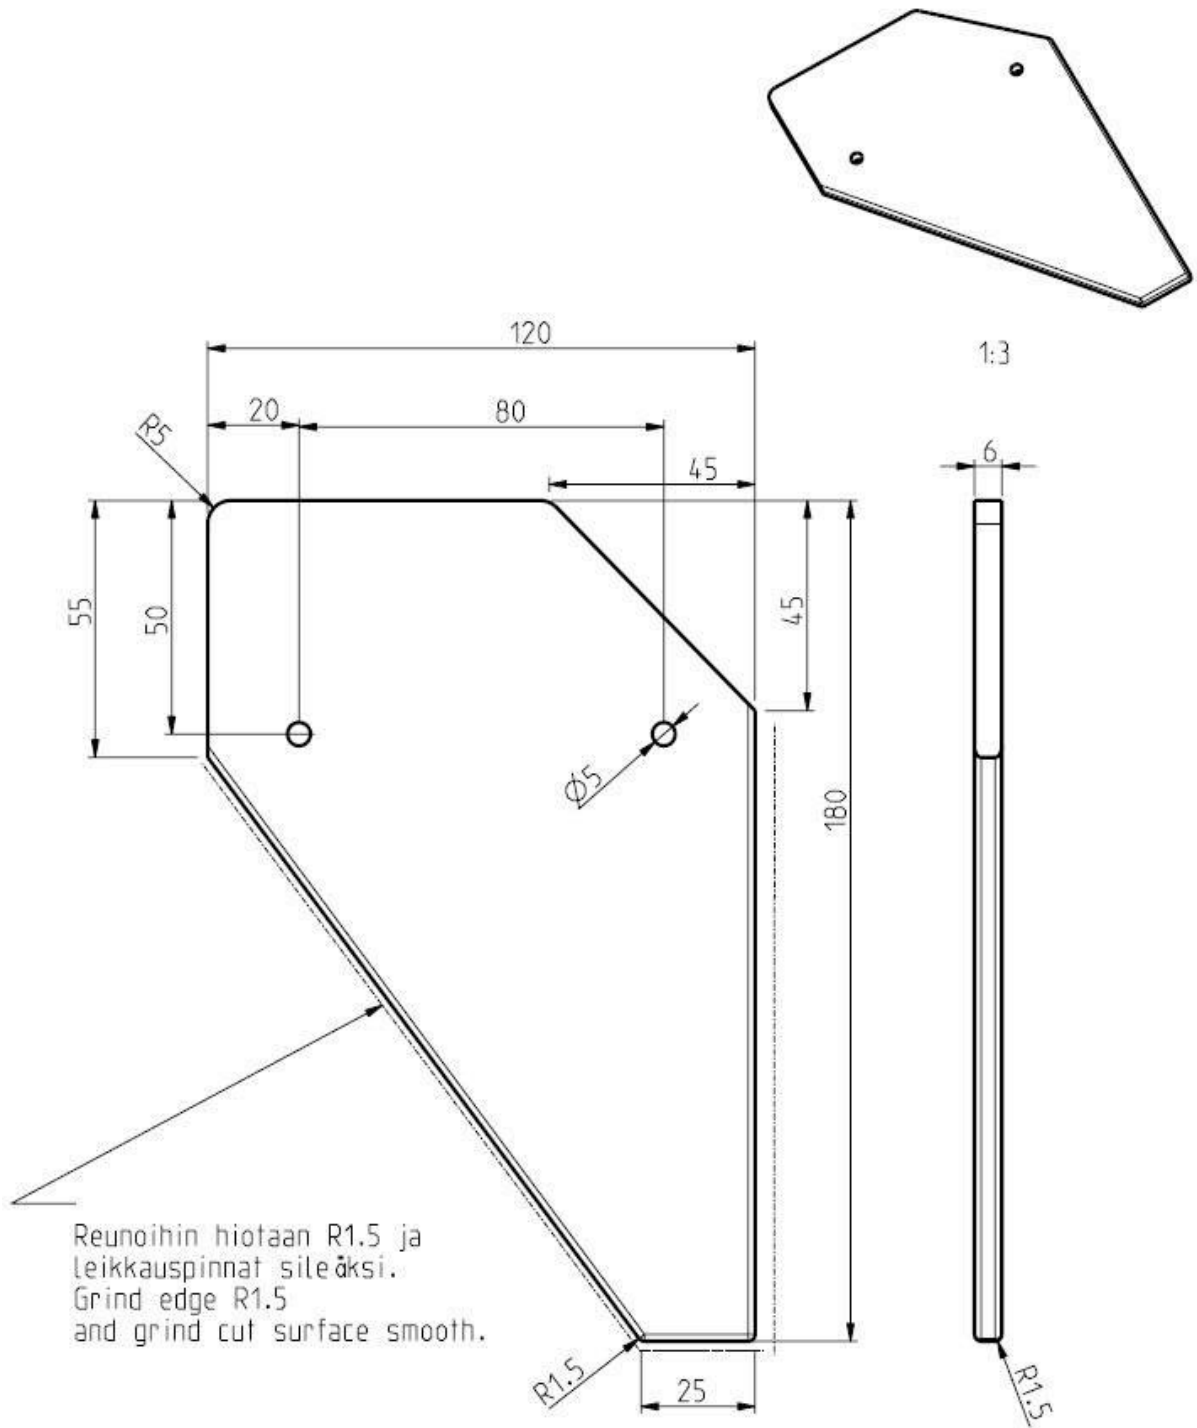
Dimensões do protetor de TI KC7 em milímetros
